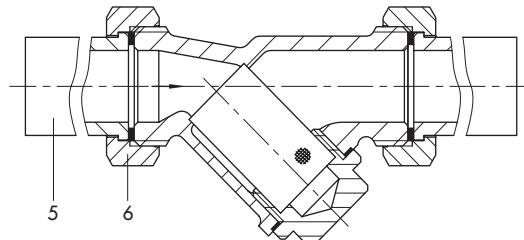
· грязеуловитель тип 1 FN, конструкция из литейной оловянно-цинковой бронзы (для установок централизованного теплоснабжения) с резьбовыми соединениями и ниппелями под приварку
